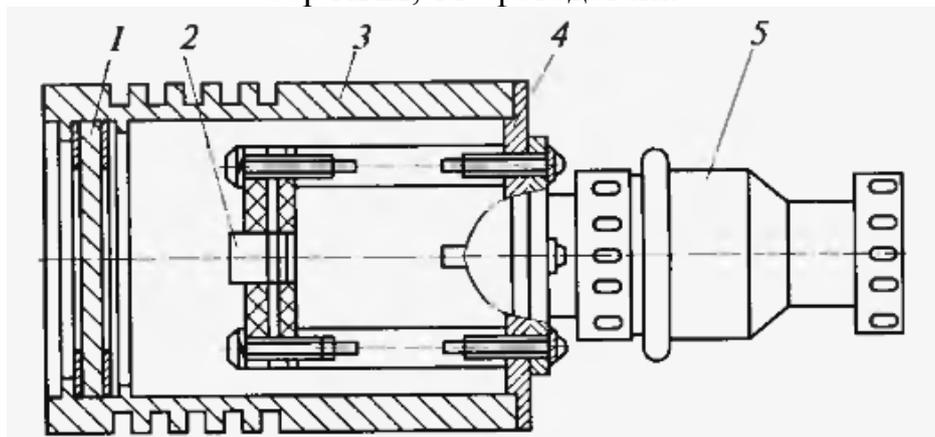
Принципиальная схема фотодатчика: 1 – стекло; 2 – фоторезистор; 3 - корпус; 4 – крышка; 5 - штепсельный разъём.
